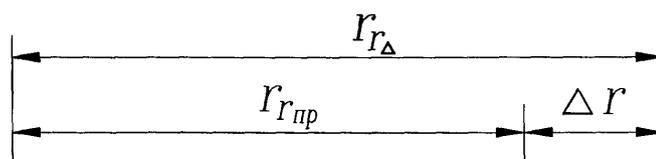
Схема размерной цепи для расчета допуска радиального биения
